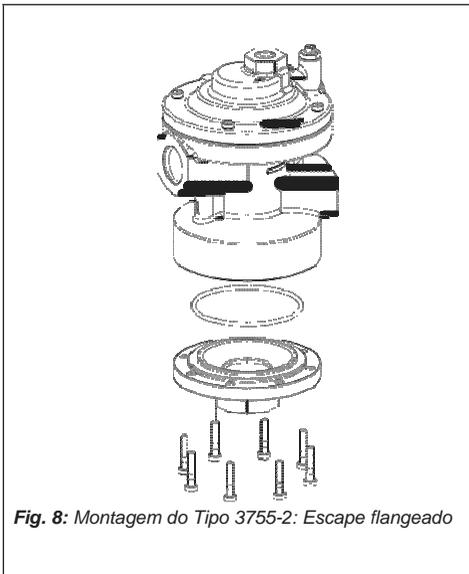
Montagem do Tipo 3755-2: Escape flangeado
